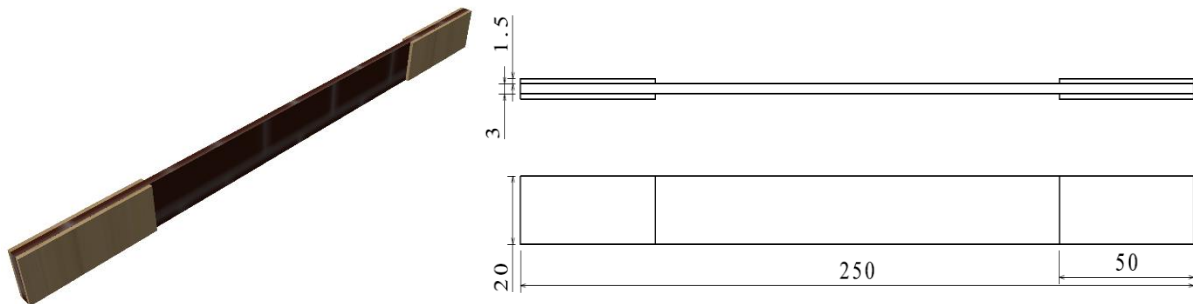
Forme et dimensions des éprouvettes de traction.
